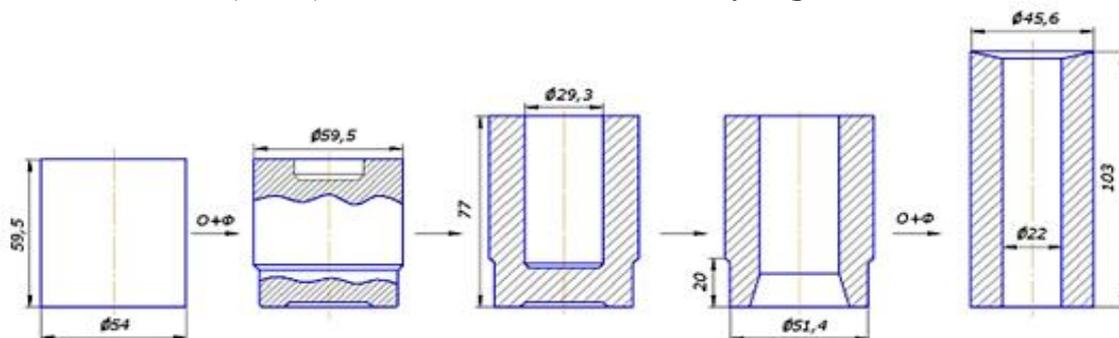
Схема изготовления поршневых пальцев ДВС и межоперационного отжига заготовки из стали 12ХН3А. О – отжиг; Ф – фосфатирование
